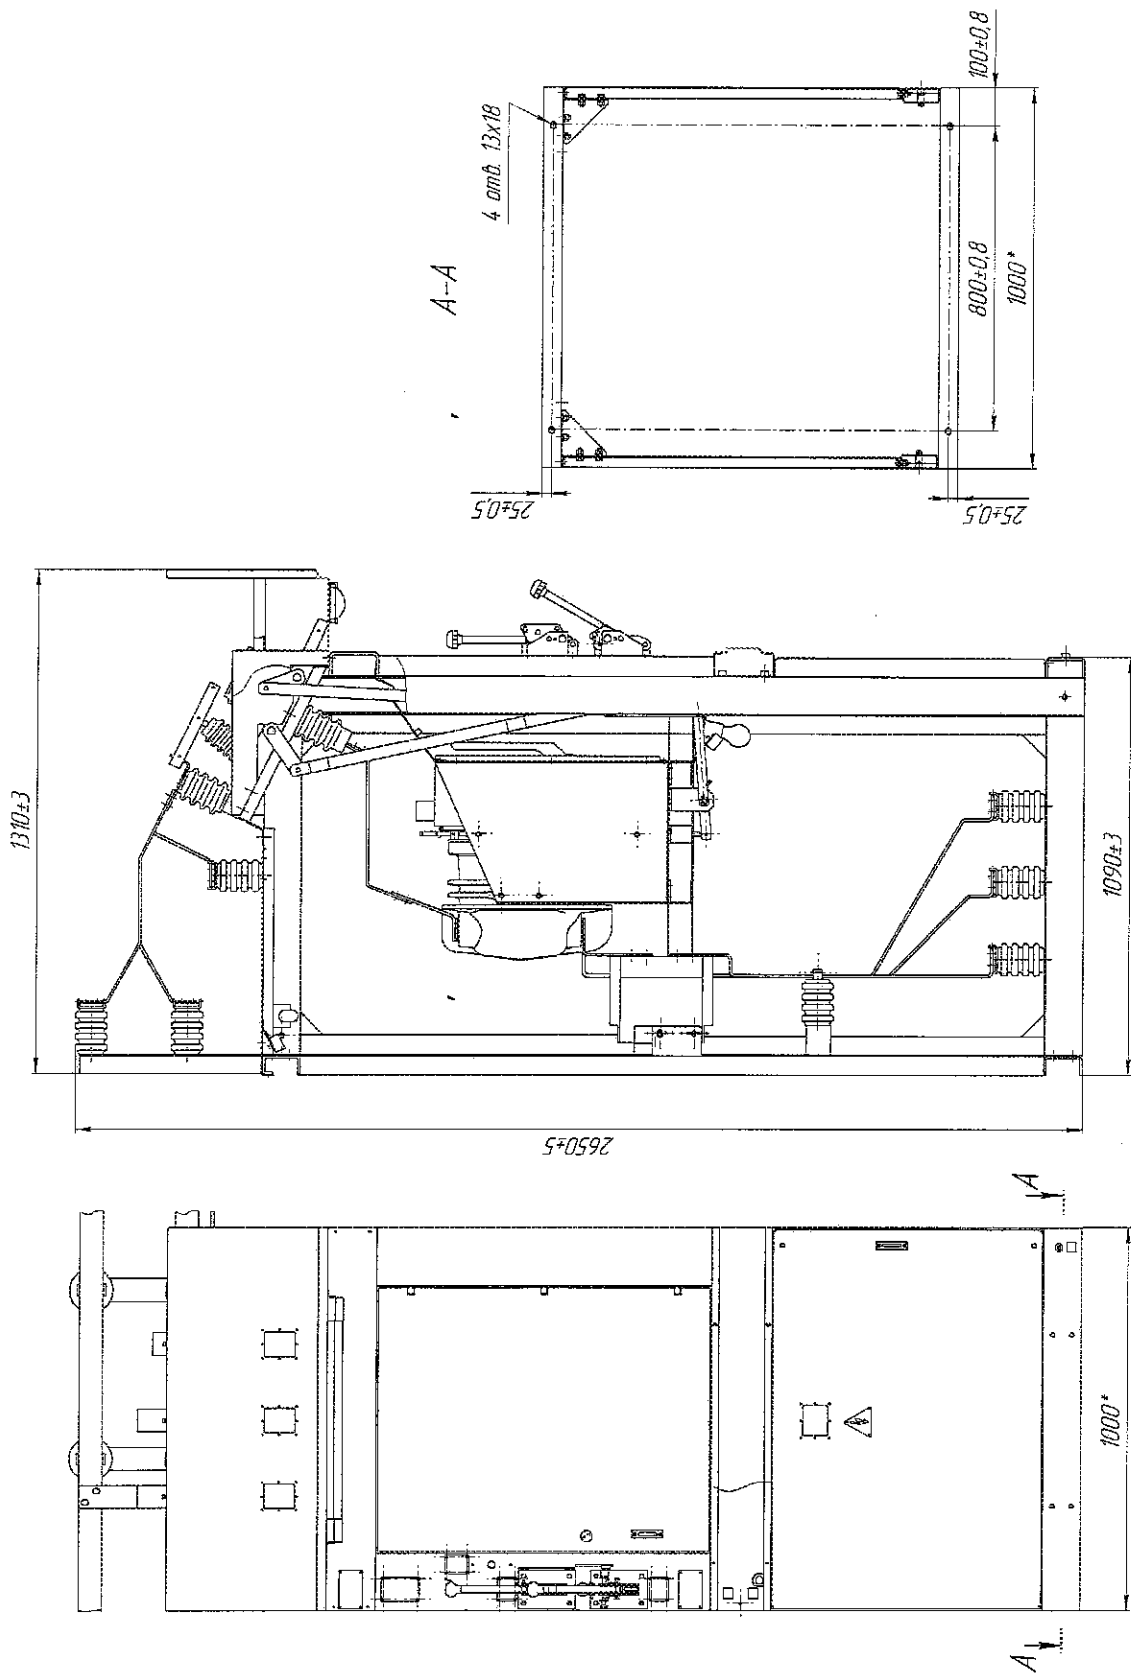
Габаритные, установочные размеры КСО-202В с выключателем LF
